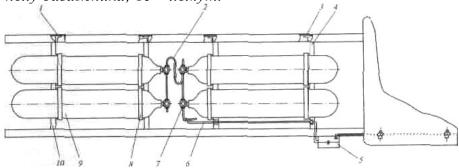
Расположение баллонов СПГ на раме автомобиля ГАЗ-3302 («Газель»): 1 и 3— крепление поперечины; 2— трубка соединительная между баллонами; 4 и 10— поперечины для крепления баллонов; 5— заправочный узел; 6— наполнительная трубка; 7— баллонный вентиль; 8 хомут; 9— баллон.
